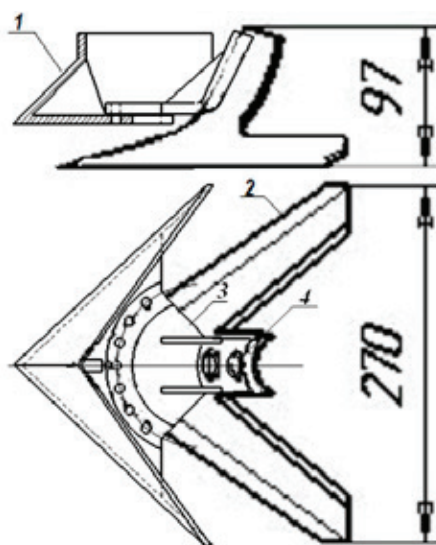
Крепление бороздооткрывателя к стойке лапы
